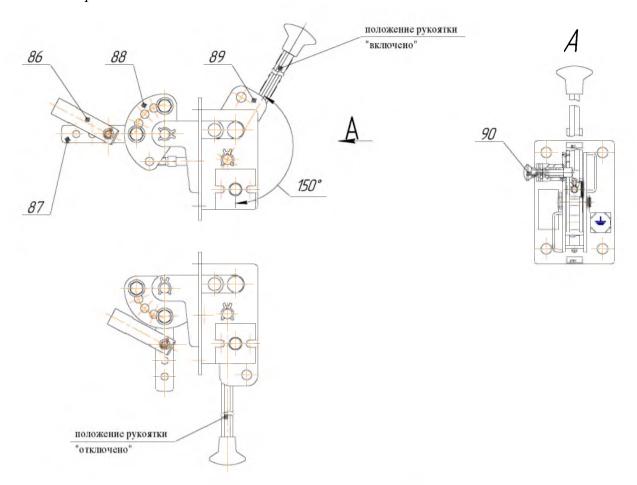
Привод ПР СЭЩ® -10 86 – вилка; 87 – пластина; 88 – секторный рычаг; 89 – рычаг; 90 – фиксатор
